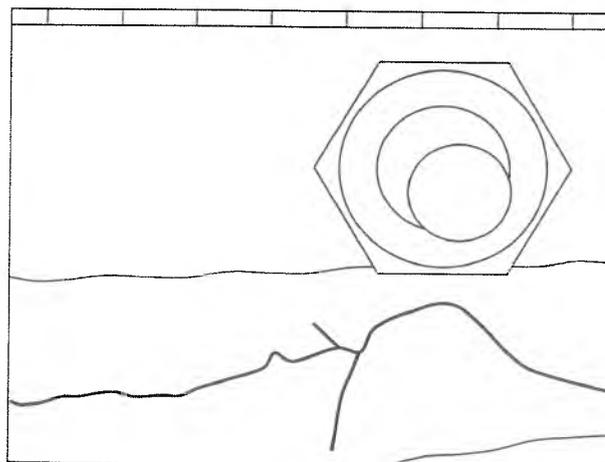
Разветвленная трещина нахлесточного сварного соединения. Общий вид
